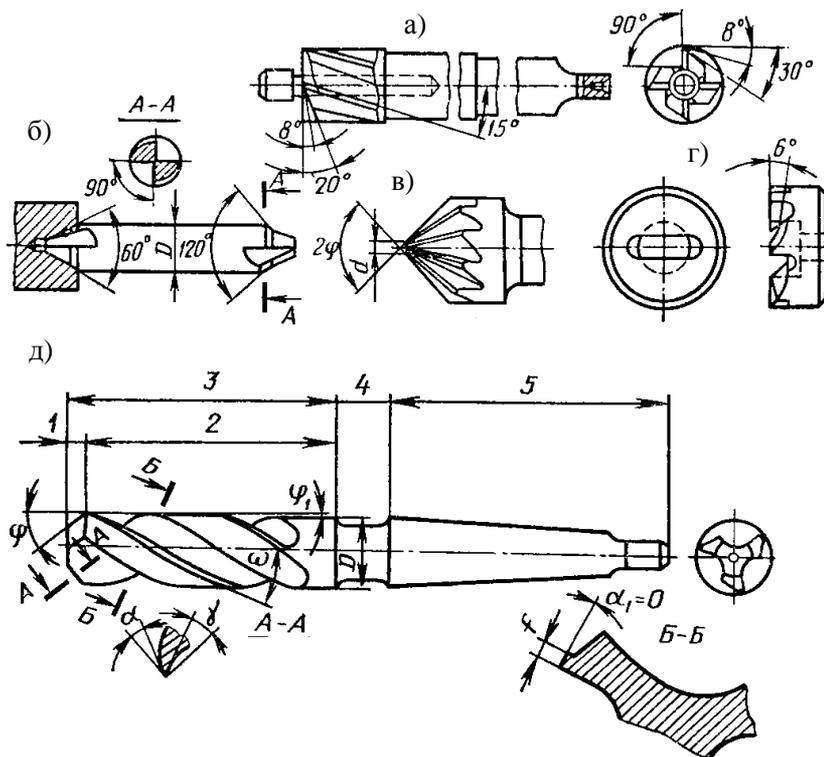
Общий вид и геометрические параметры режущей части цековок (а), зенковок (б, в) и зенкеров (г, д)
